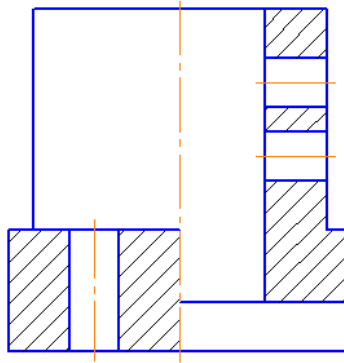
Разрез Б–Б на чертеже детали
